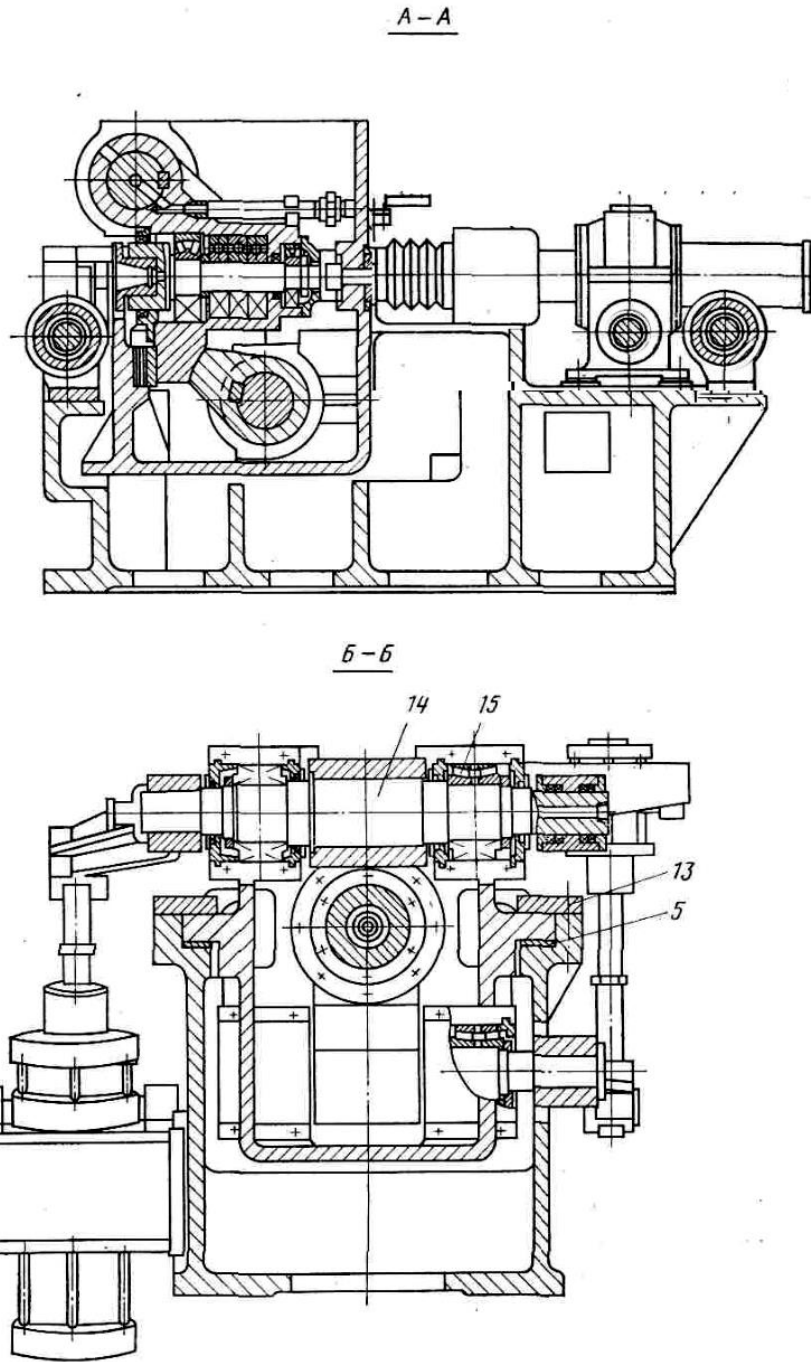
Упорно-регулювальний механізм (розрізи по рис.9.7)
